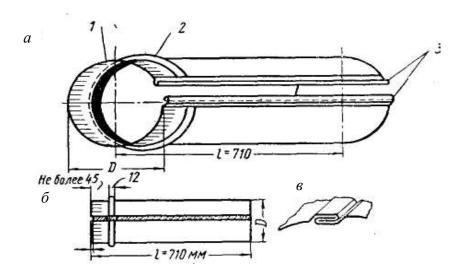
Стадии изготовления прямошовного газохода: a — общий вид звена после обработки;  $\delta$  — звено воздуховода с закатанным швом;  $\epsilon$  — соединение продольного фальца; l — гофрированный конец звена; l — валик жесткости (зиг); l — лежачие фальцы
